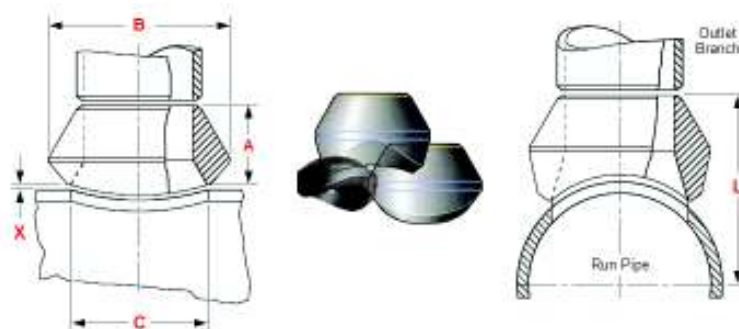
Dimensiones del elemento soldable (Weldolet).
